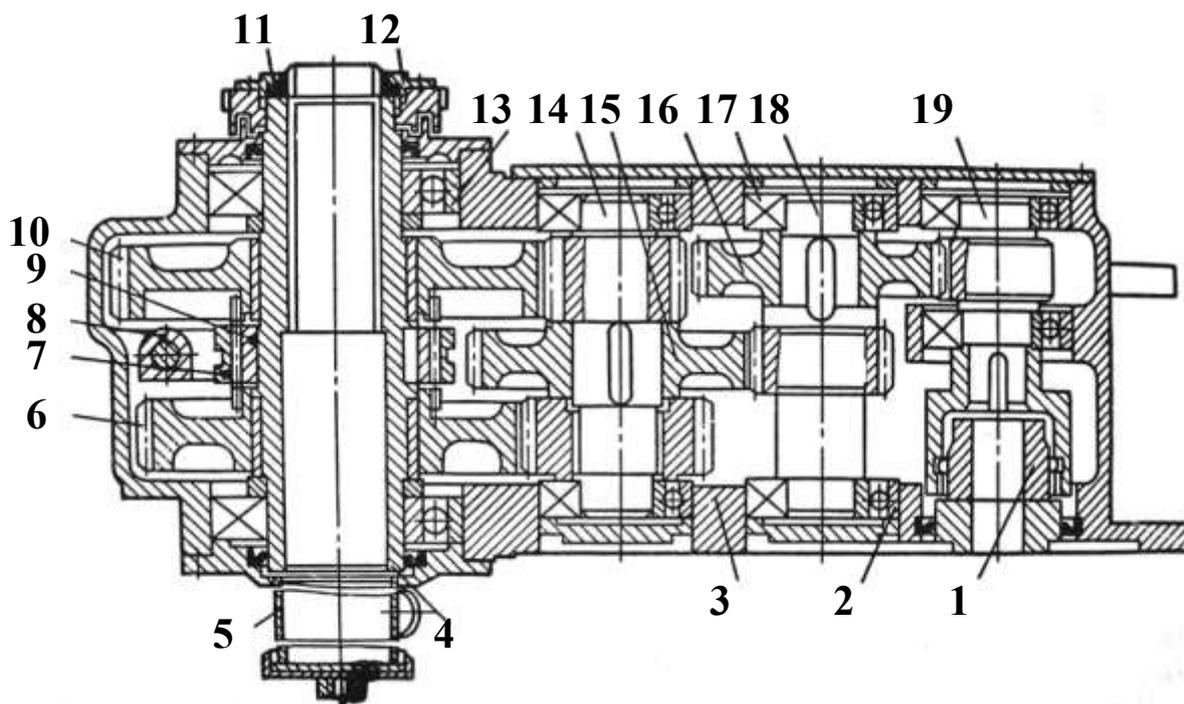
Редуктор станка буровой установки БГА-4М
